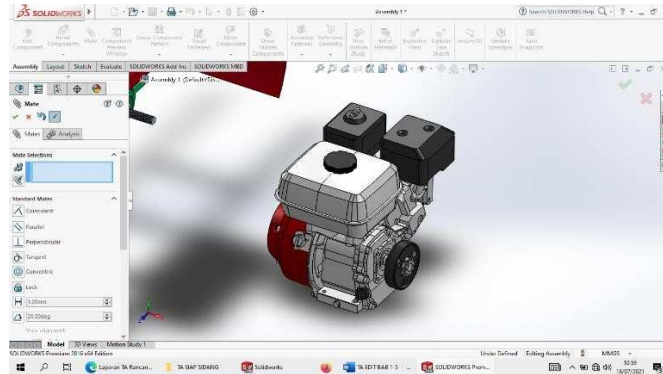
146 Hasil *Assembly* Kerangka dan Poros Roda
